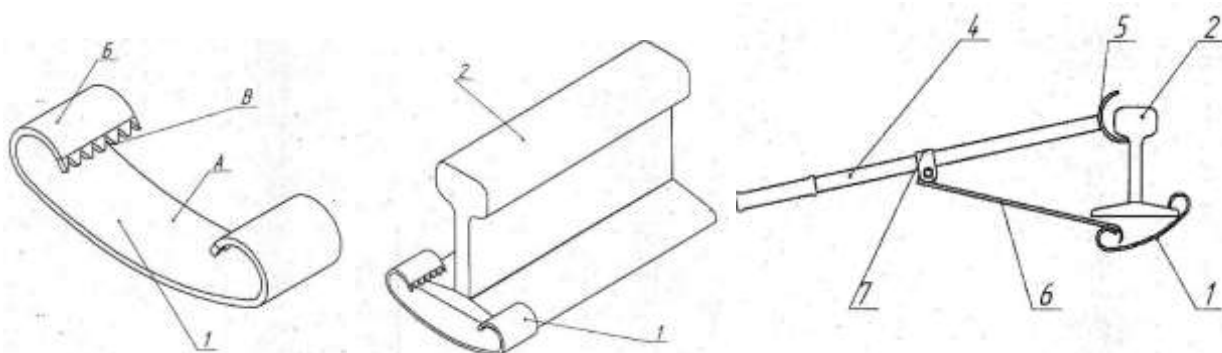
Предлагаемый новый рельсовый соединитель и ключ для его установки
